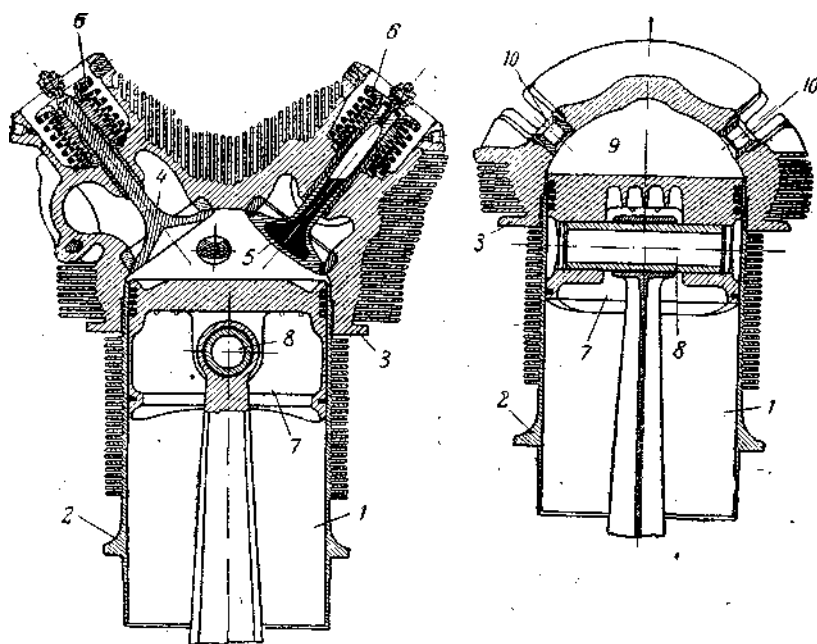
Цилиндр двигателя воздушного охлаждения:
